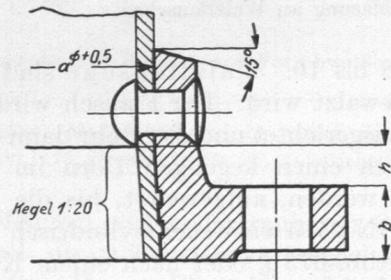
Walzflansch mit Sicherheitsnietung. Kegelige Flanschbohrung.
